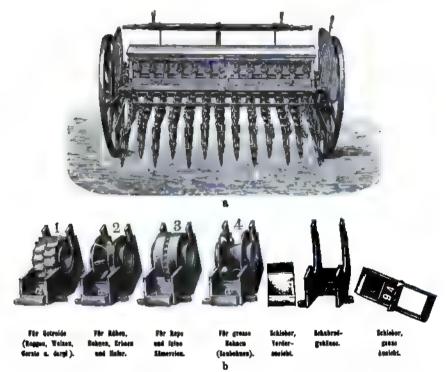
a Drillmaschine mit Schubradsystem von Fr. Dehne-Halberstadt, b die verschiedenen Schubräder zu dieser Drillmaschine.
